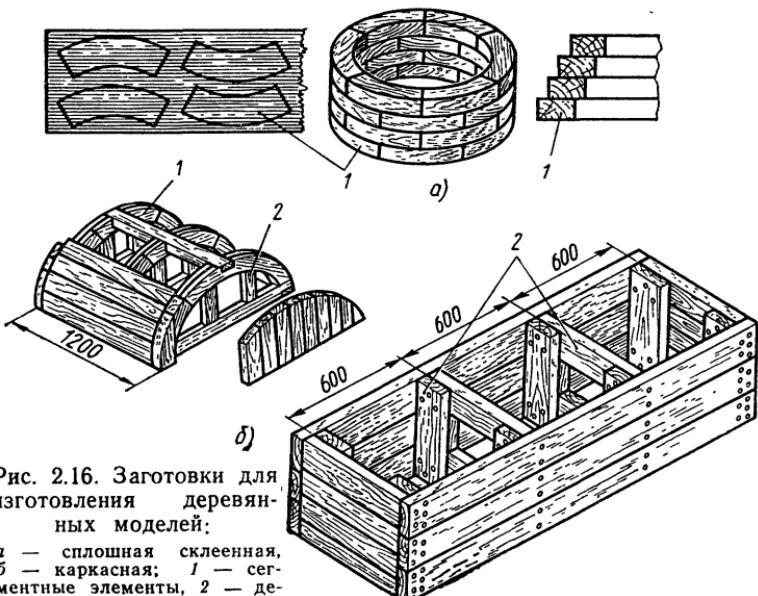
Заготовки для изготовления деревянных моделей:
